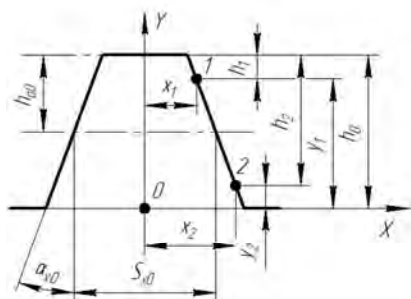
Профиль зуба фрезы по передней поверхности
